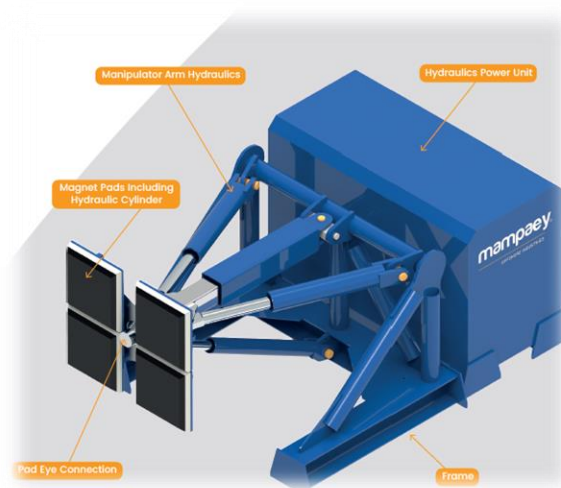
Конструкции системы швартовки «The intelligent Dock Locking» [15]
